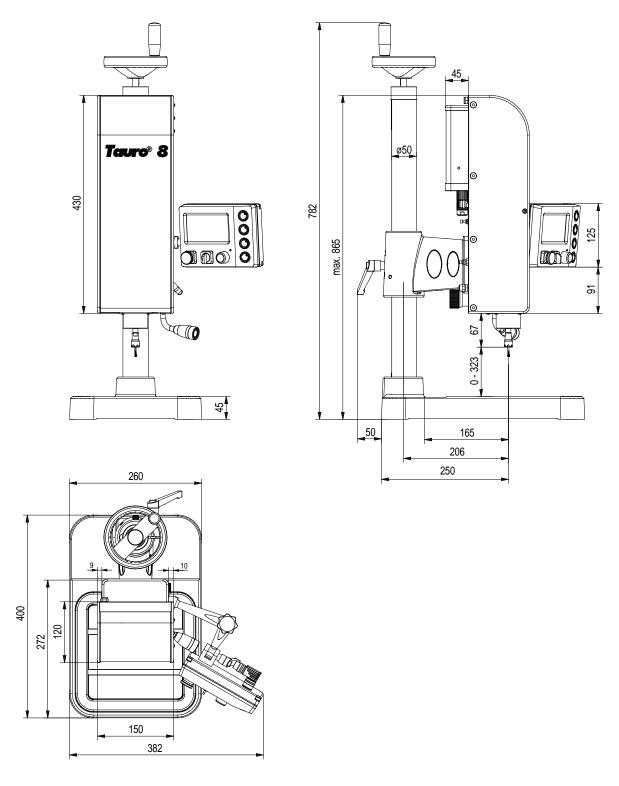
Vues de la machine à usiner les filets Tauro 8
